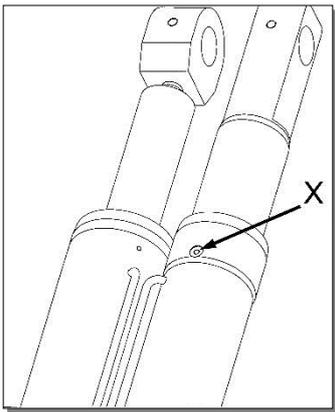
Pos. X = Entlüftungsschraube jeweils an den Folgezylindern
